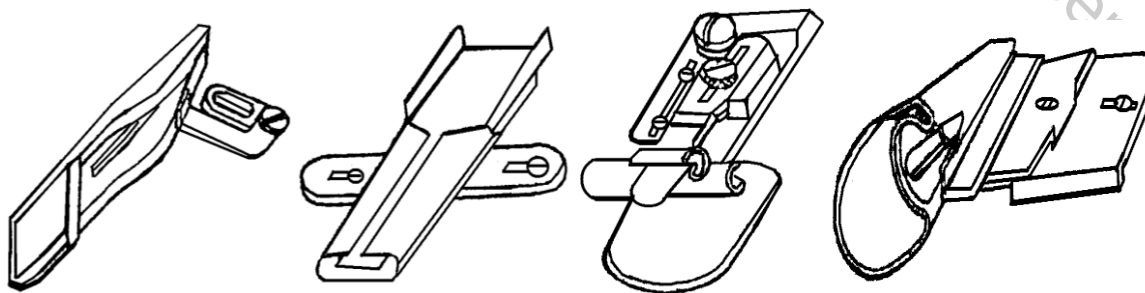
Спецприспособления для изготовления шлевок, съемных поясов, ремешков и тому подобных деталей
